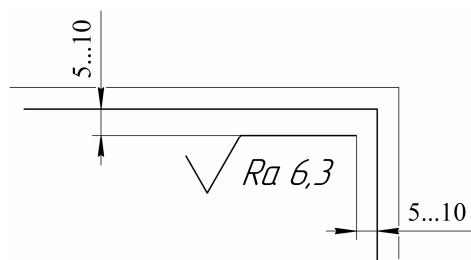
Пример обозначения шероховатости для всех поверхностей изделия
